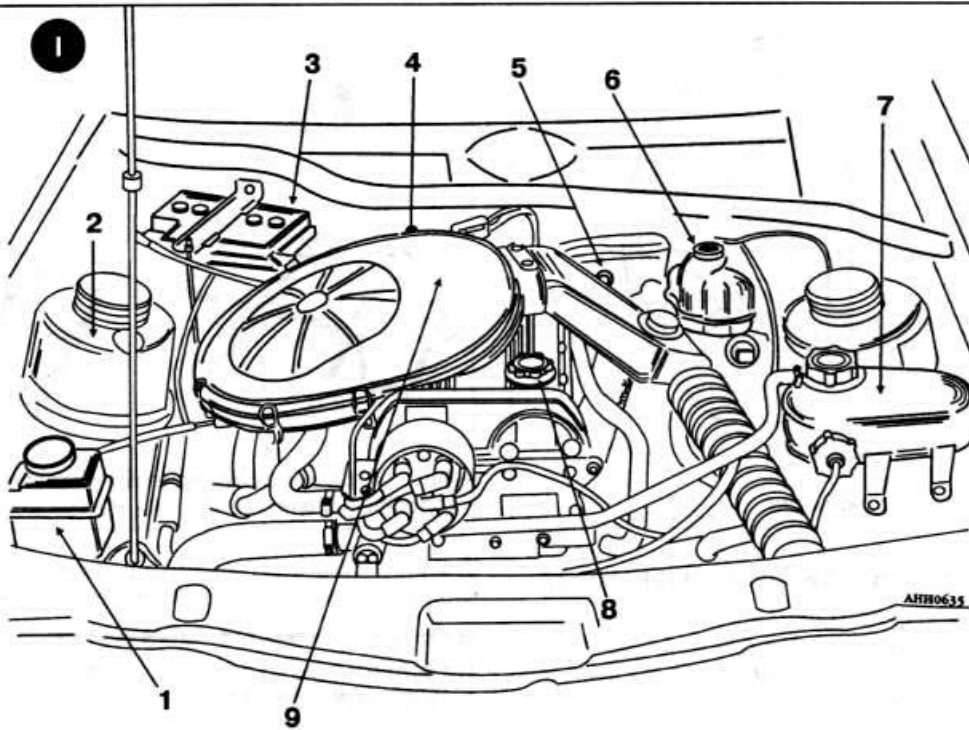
Вид моторного отсека с двухвальными бензиновыми двигателями:
